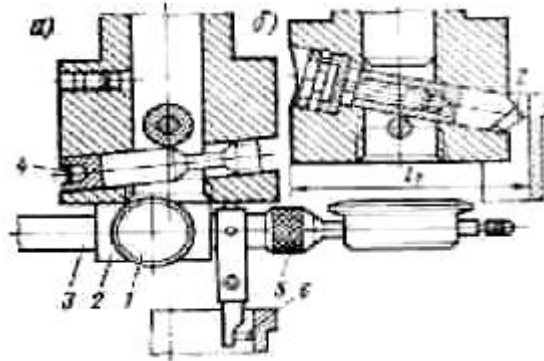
Різцева головка верстата 2А78Н з пристосуваннями для центрування гільз (а) і установки різця (б)
